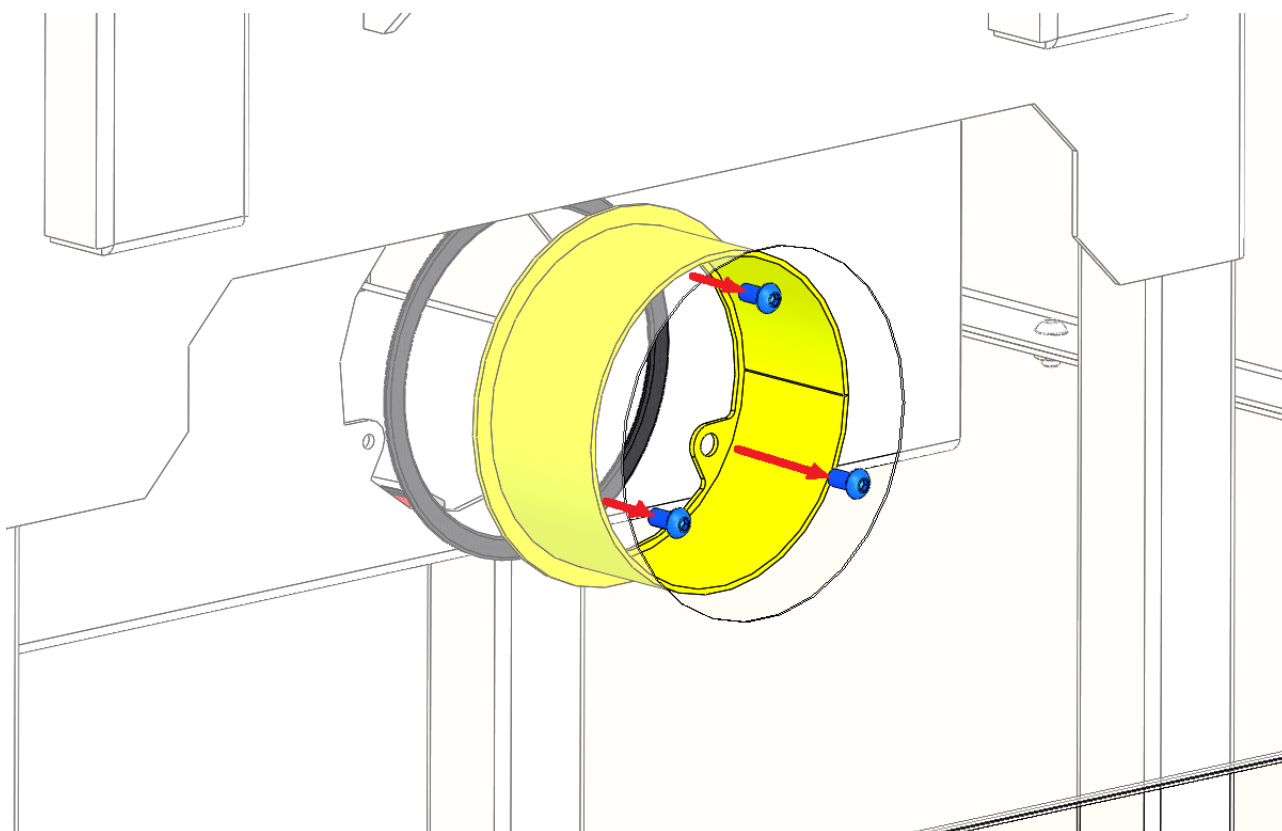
Rimozione del collegamento per l'alimentazione d'aria esterna
